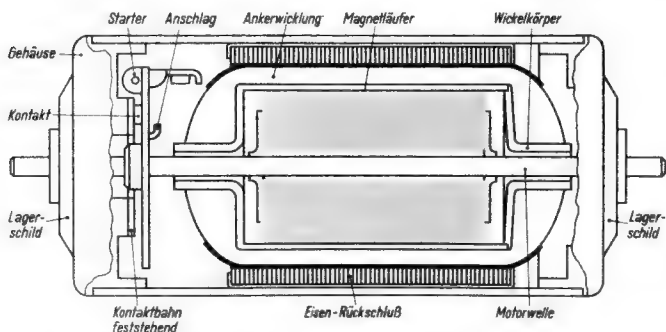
Schnittzeichnung des kollektorlosen Kleinstmotors
